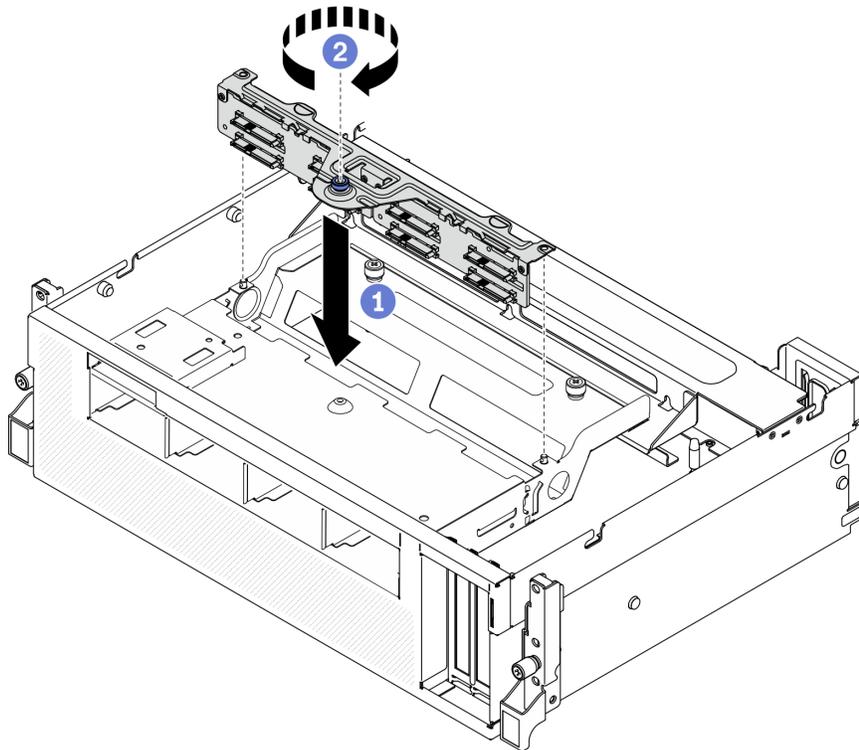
Installation du module du fond de panier d'unité 2,5 pouces
